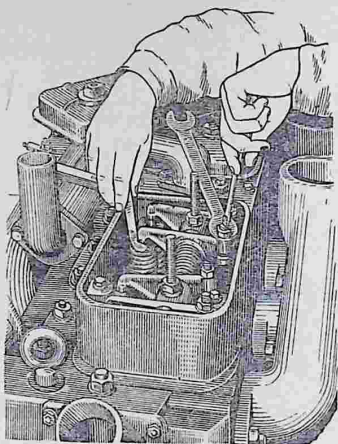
Регулировка тепловых зазоров в механизме газораспределения двигателя Д-54А.
